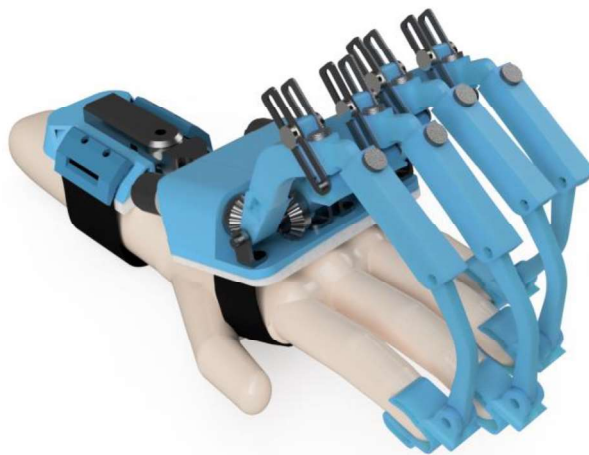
Mecanismo para los dedos trifalángicos. Se observa el mecanismo diseñado en [5] en conjunto con la mano. Los eslabones del mecanismo unidos a la punta del dedo, y por el otro lado se unen a los engranes que son movidos por el motor.
